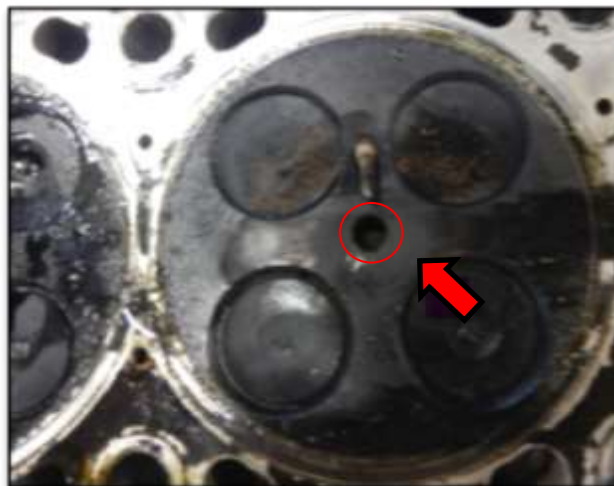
Poškozená hlava válců motoru MZ-CD [51]
